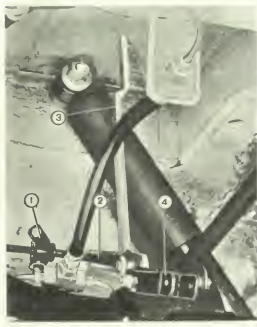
Установка приспособления А.72245 (или 67.7820-9518) для регулировки положения регулятора давления задних тормозов: 1 — иронштейн рычага привода регулятора давления; 2 — рычаг привода регулятора давления; 3 — приспособление А.72245 (или 67.7820-9518); 4 — тяга, соединяющая рычаг привода регулятора давления с иронштейном балки заднего моста.
